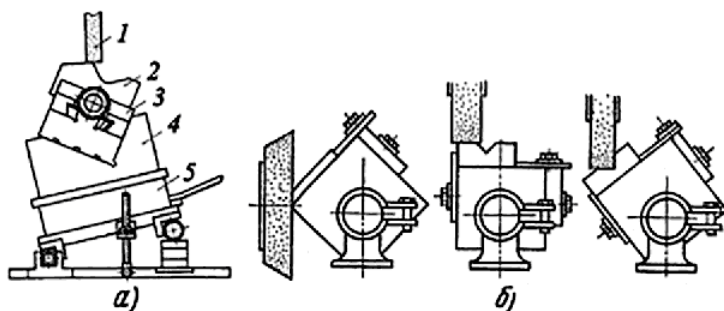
Шлифование различных поверхностей с синусным приспособлением:
